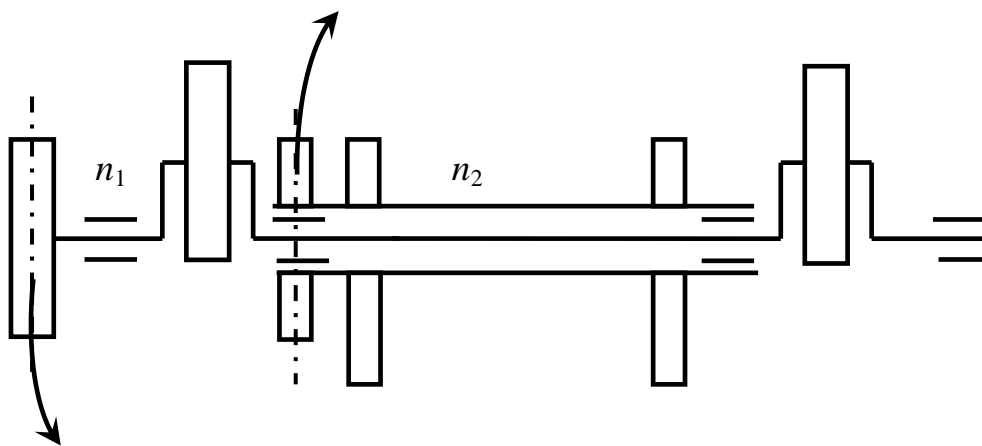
Схема соосного вала привода механизма очистки зерноуборочного комбайна
